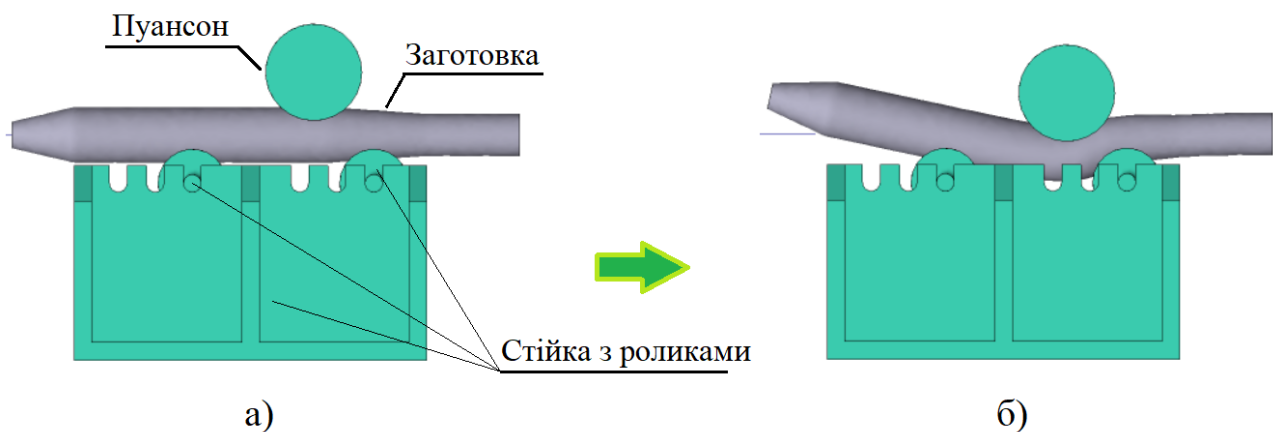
3D-модель процесу згинання заготовки гака початкове положення заготовки перед згинанням (а) та положення заготовки після здійснення першого етапу згинання (б)
